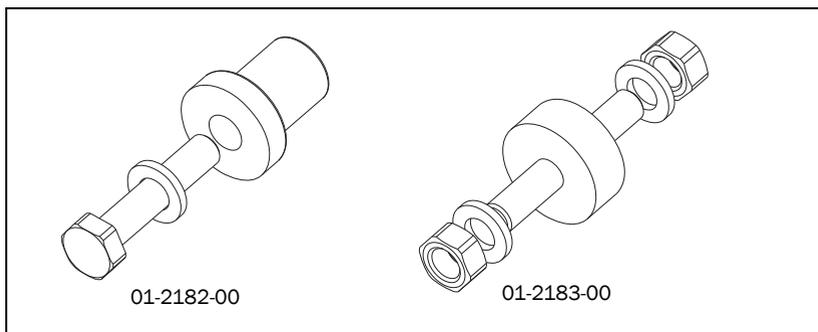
Montagesätze mit Schwingungsdämpfung für den Motor
